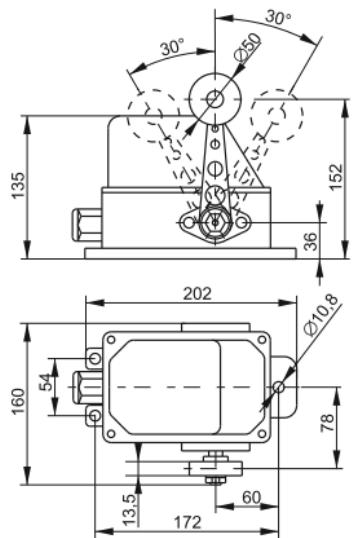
Габаритные и установочные размеры выключателей КУ-701 У1
